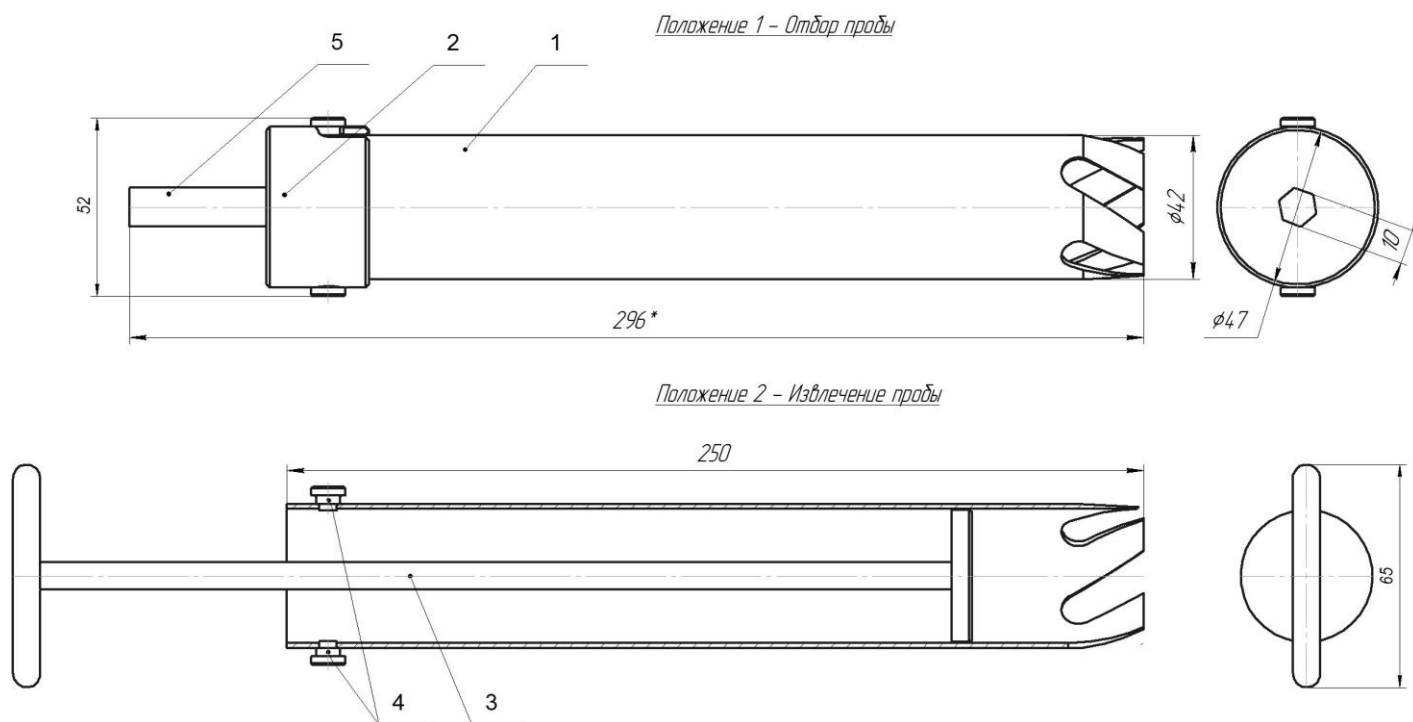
Эскиз пробоотборника типа ППМ: 1 – корпус; 2 – конус; 3 – направляющая втулка; 4 – упор; 5 – шток; 6 – ручка; 7 – пробка; 8 – гайки.
